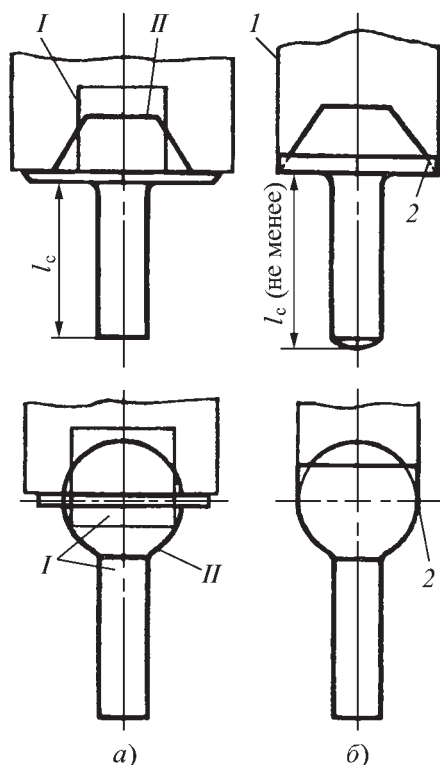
Поковки с конической и шаровидной головками, получаемые в штампах:
